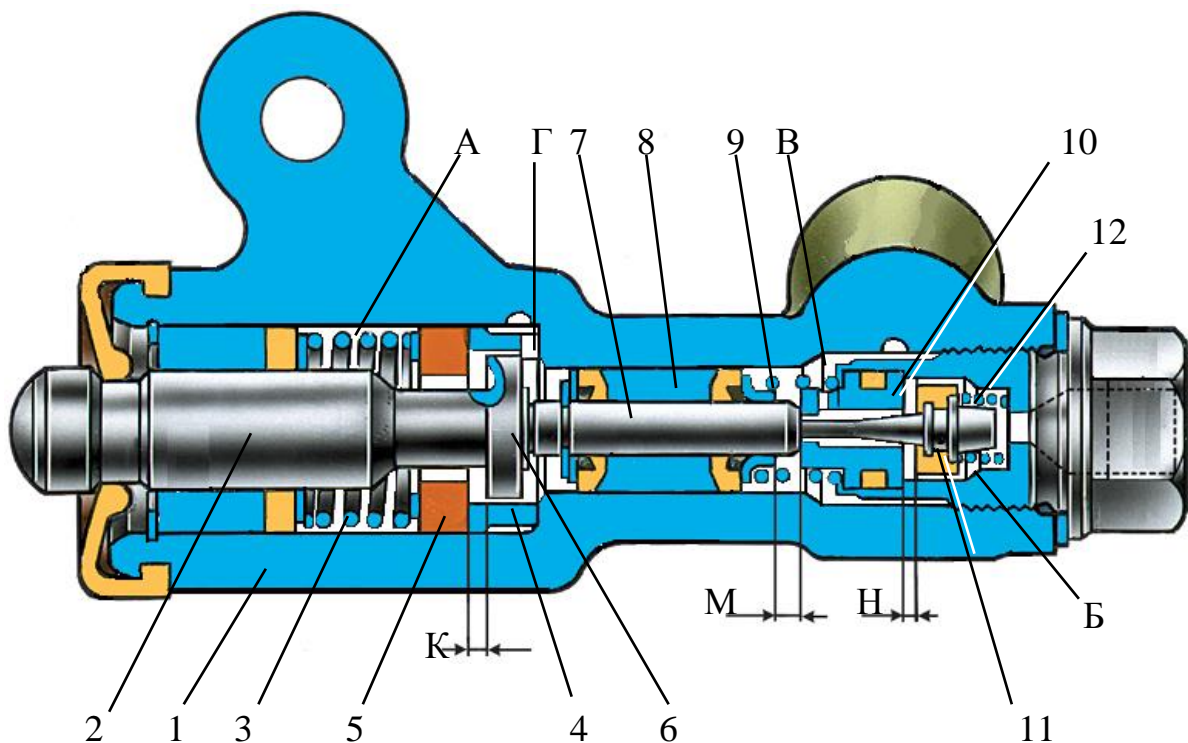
Конструкция регулятора тормозных сил переднеприводного автомобиля с диагональным разделением тормозного привода на два контура: 1 – корпус регулятора давления; 2 – поршень; 3 – пружина; 4 – втулка корпуса; 5 – уплотнитель головки поршня; 6 – головка поршня; 7 – толкатель; 8 – втулка толкателя; 9 – пружина втулки толкателя; 10 – седло клапана; 11 – клапан; 12 – пружина клапана; А, Б – полости, соединенные с главным цилиндром; В – полость, соединенная с рабочим цилиндром правого заднего колеса; Г – полость, соединенная с рабочим цилиндром левого заднего колеса; К, М, Н – зазоры
